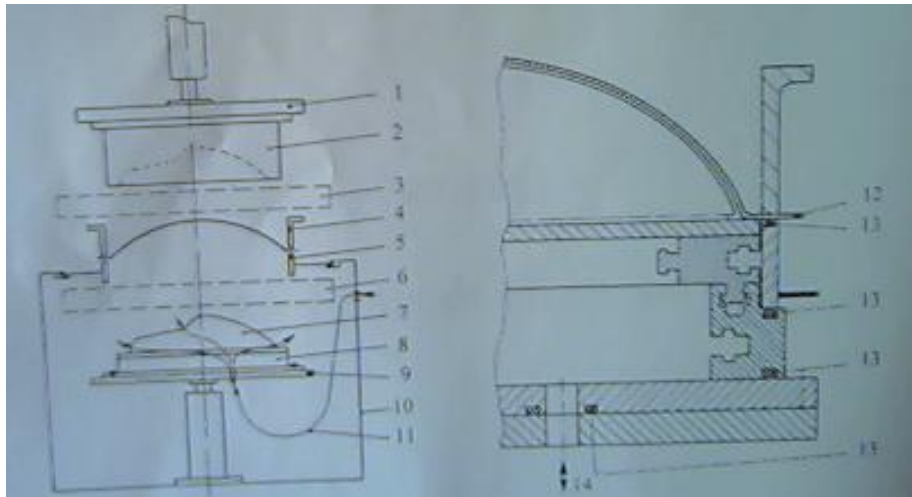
a) Poste de formage d'une machine de thermoformage universelle ;
